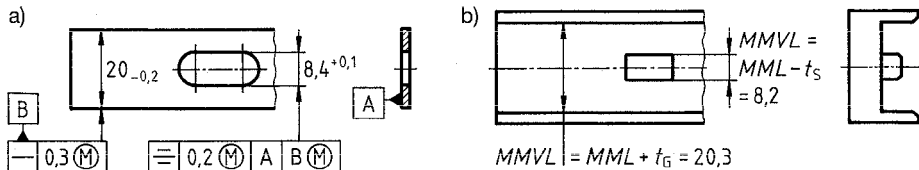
Prüfung eines Fensterbeschlagblechs. a) Zeichnung (Ausschnitt), Bezugselement mit Geradheitstoleranz und MMB; b) Prüflehre dazu
